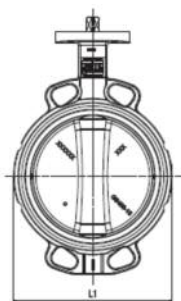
Габаритные и присоединительные размеры затворов типа SYLAX.
